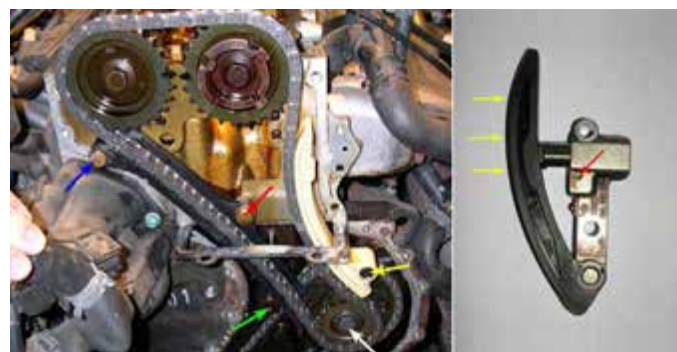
Гидравлический натяжитель втулочно-роликовой цепи привода распределительного вала; источник: *VW
